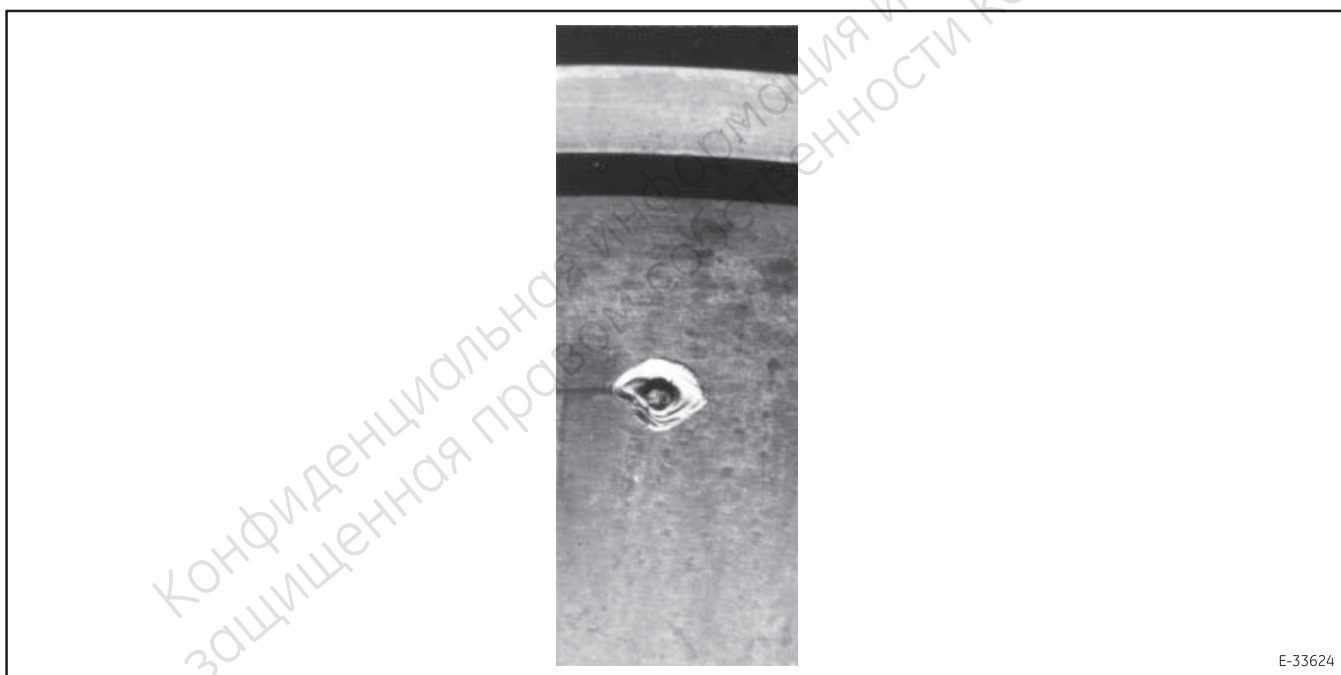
Наружное кольцо подшипника с признаками шелушения или "размазывания" поверхности
